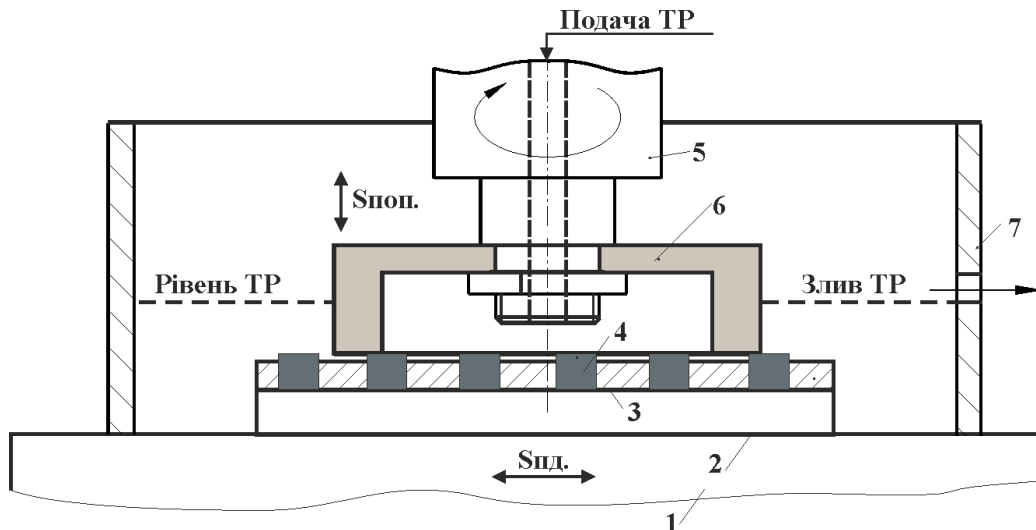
Схема плоского торцевого шліфування з подачею ТР у внутрішню порожнину круга через полий шпиндель
